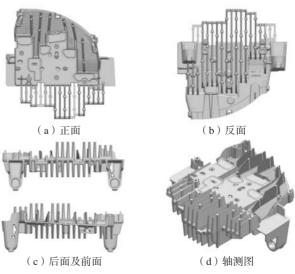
车灯支架铸件结构 Fig. 1 Structure of the car lamp holder casting
